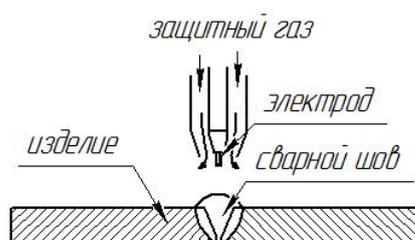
Схема сварки неплавящимся электродом в среде защитного газа
